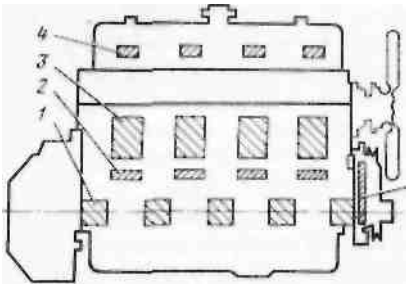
Зони прослуховування двигуна: 1 - підшипники колінчастого вала; 2 - підшипники розподільного вала; 3- поршнева група; 4 - клапани; 5 - розподільні шестірни
